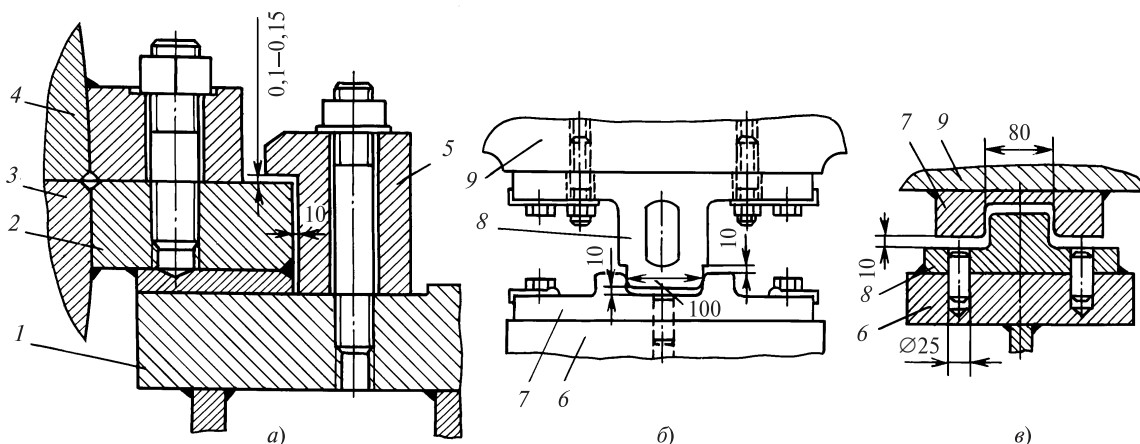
Детали установки обоймы в корпусе ЦНД
